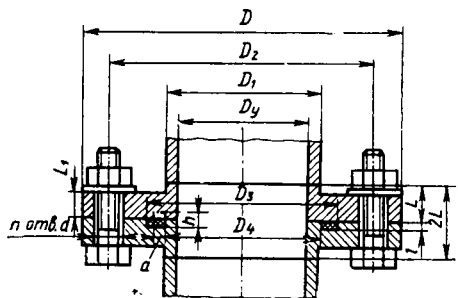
Конструкции разборного соединения с несимметричными фланцами и резиновыми прокладками
